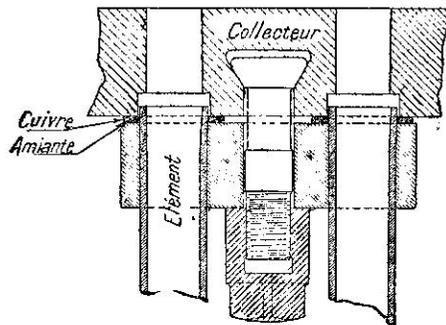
Assemblage d'un élément de surchauffe et du collecteur.
